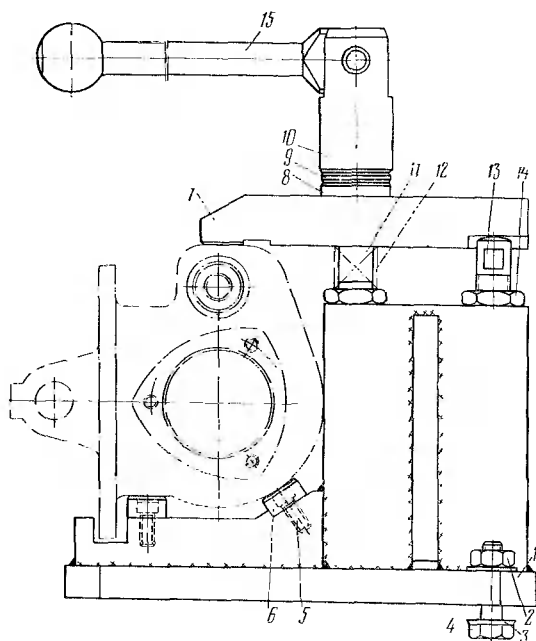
Приспособление для разборки и сборки коробки отбора мощности:
